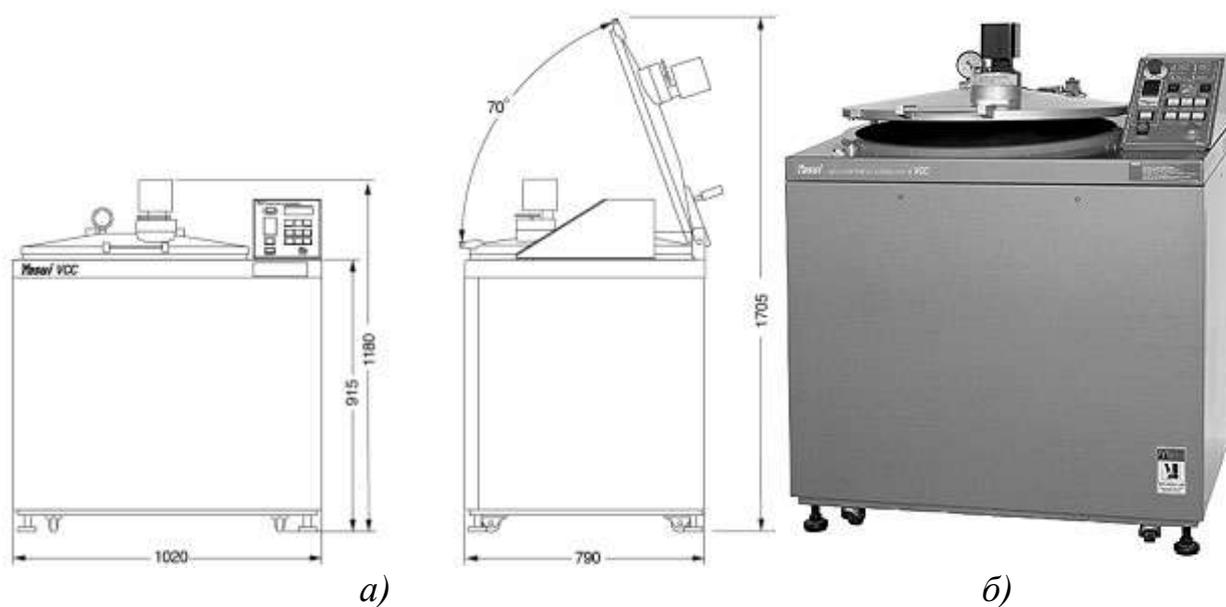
Схема блока центробежного литья «Man-neutor»
